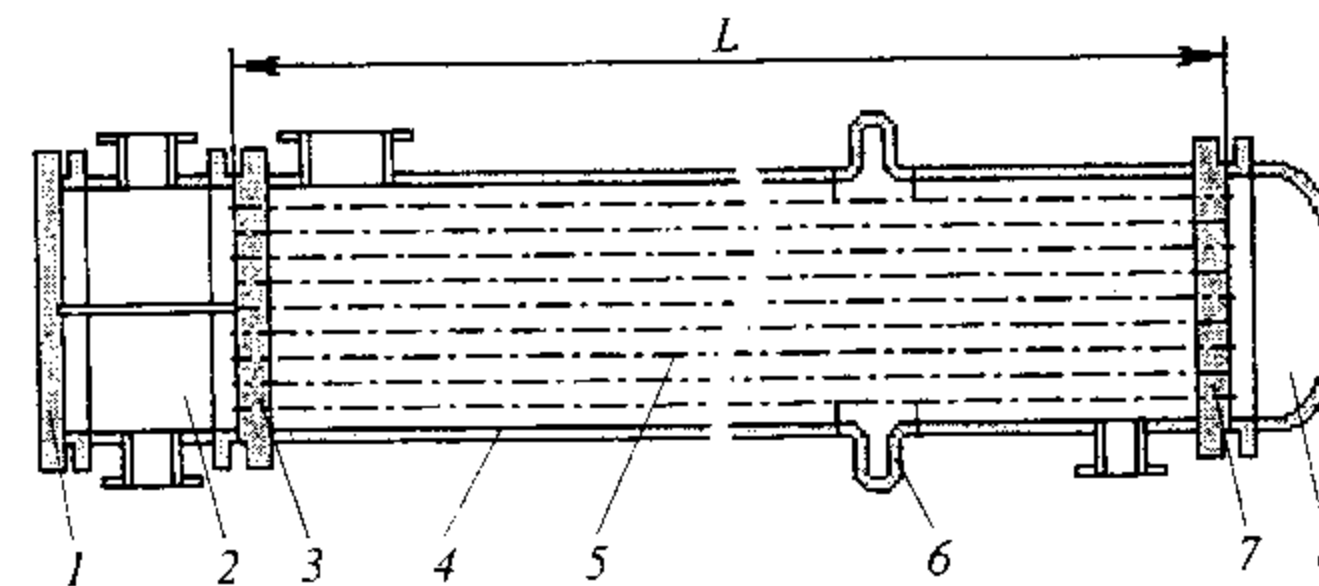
Кожухотрубчатый двухходовой конденсатор:
